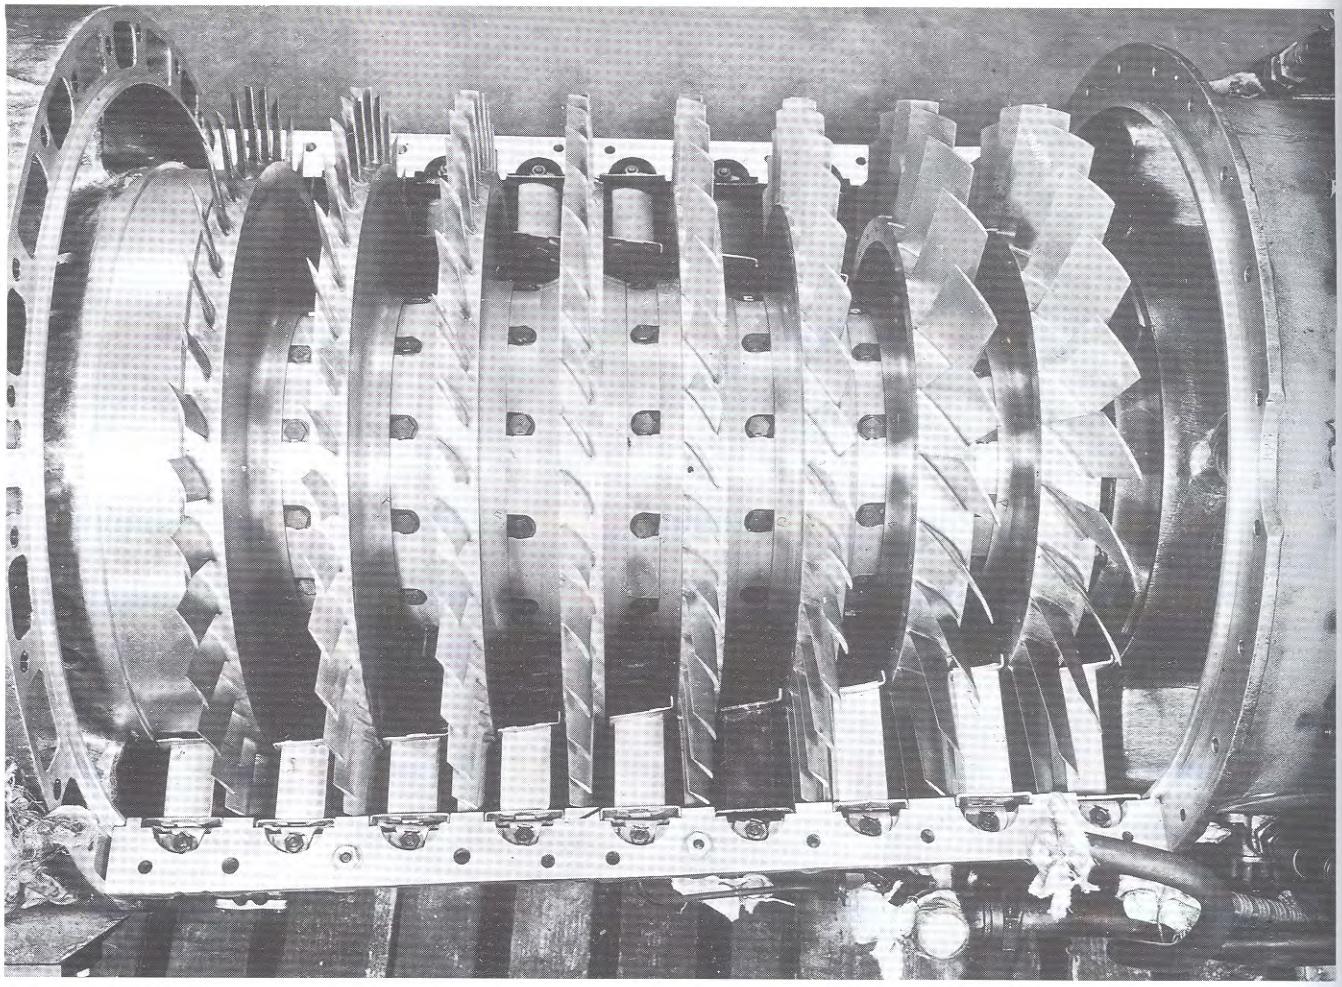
Вид сверху на ротор компрессора двигателя Юнкерс 109-004 В-1. Воздухозаборник справа (не показан)
